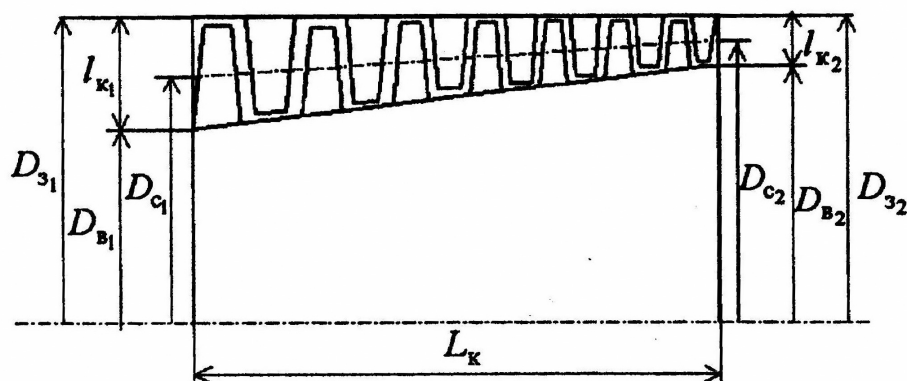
Меридіанний переріз проточної частини компресора ГТД
